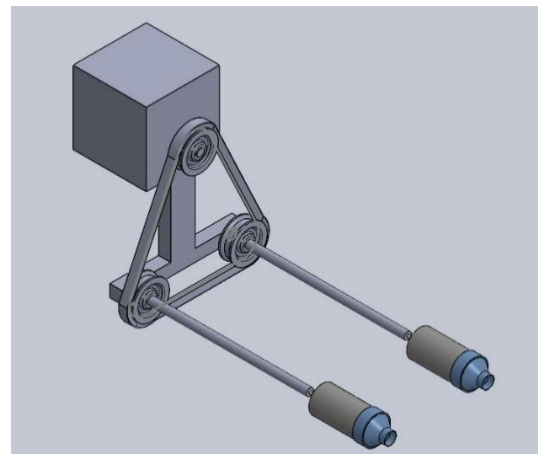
Desain Komponen Utama *Waterjet Thruster (inlet, impeller, & outlet)
